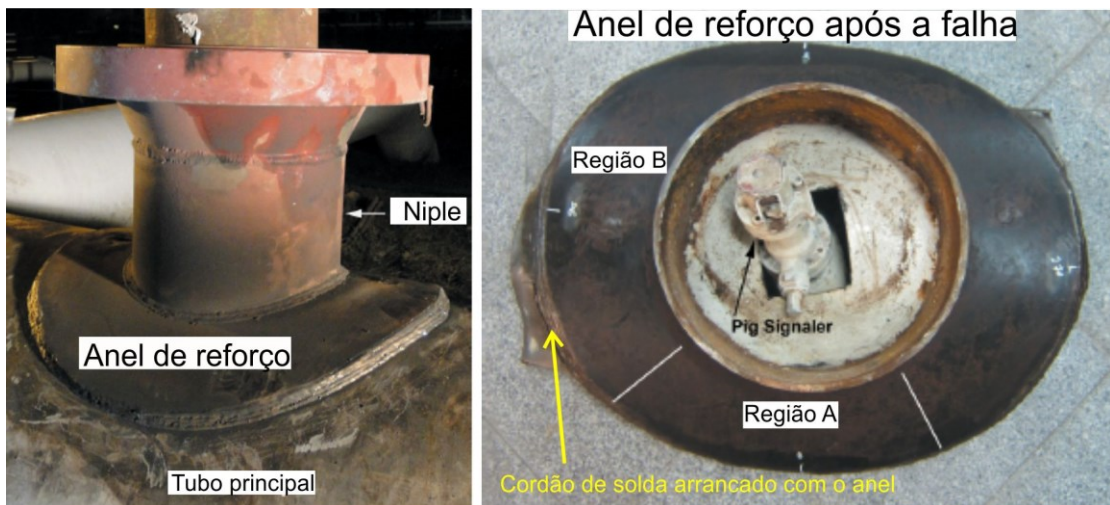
Falha em solda em operação realizada por SMAW. Em) Anel de vedação soldado, antes da falha; b) Anel rompido do tubo após a falha. Adaptado de Fazardi [27].
